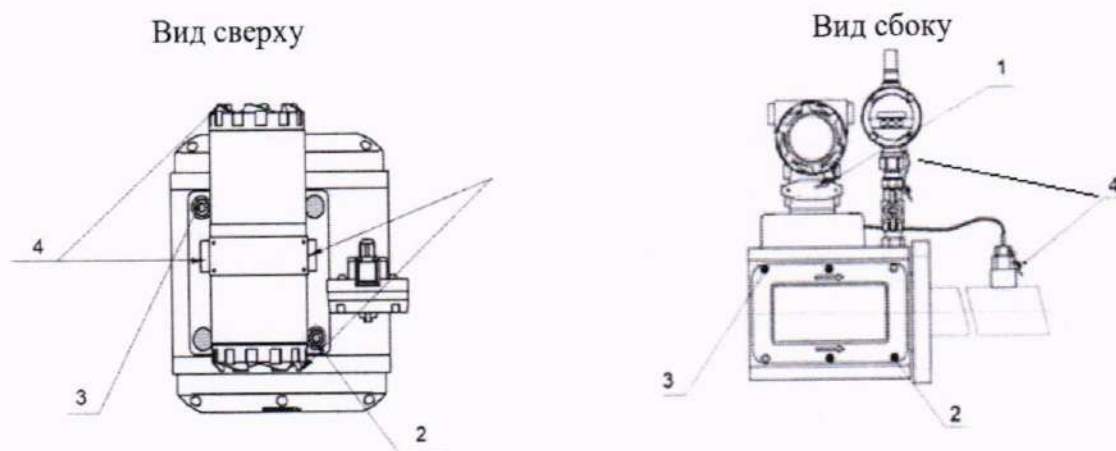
Корпус прямоугольного сечения с совмещенными защитными крышками
